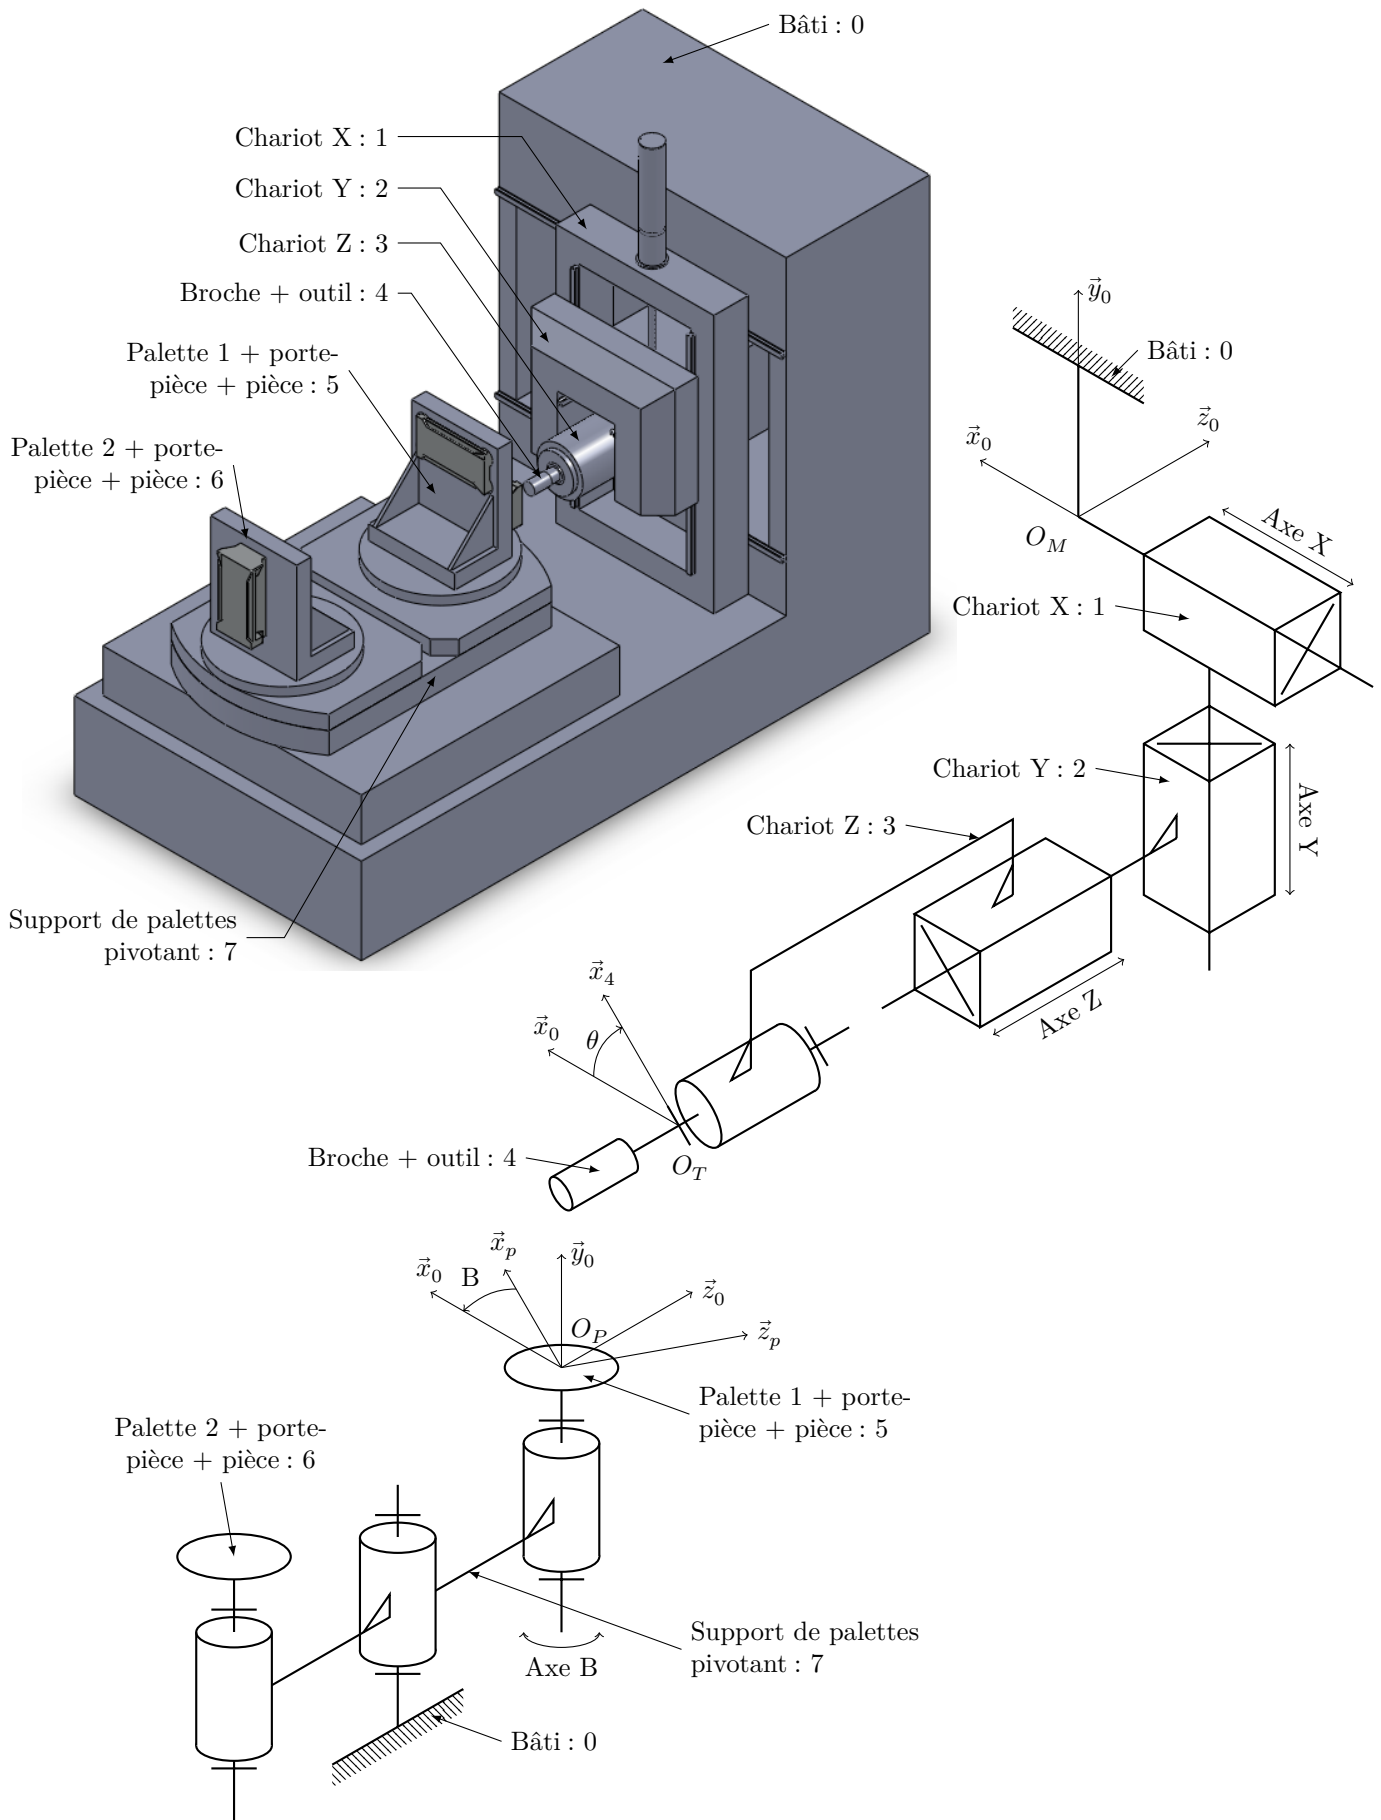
Vue éclatée de la machine pour les axes X, Y et Z
